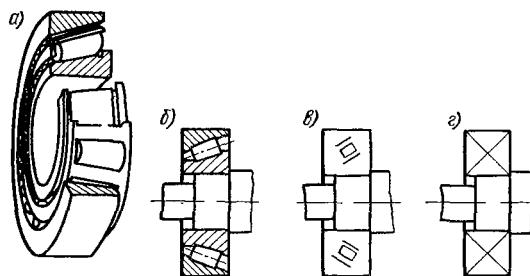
Радиально-упорный роликовый однорядный подшипник
